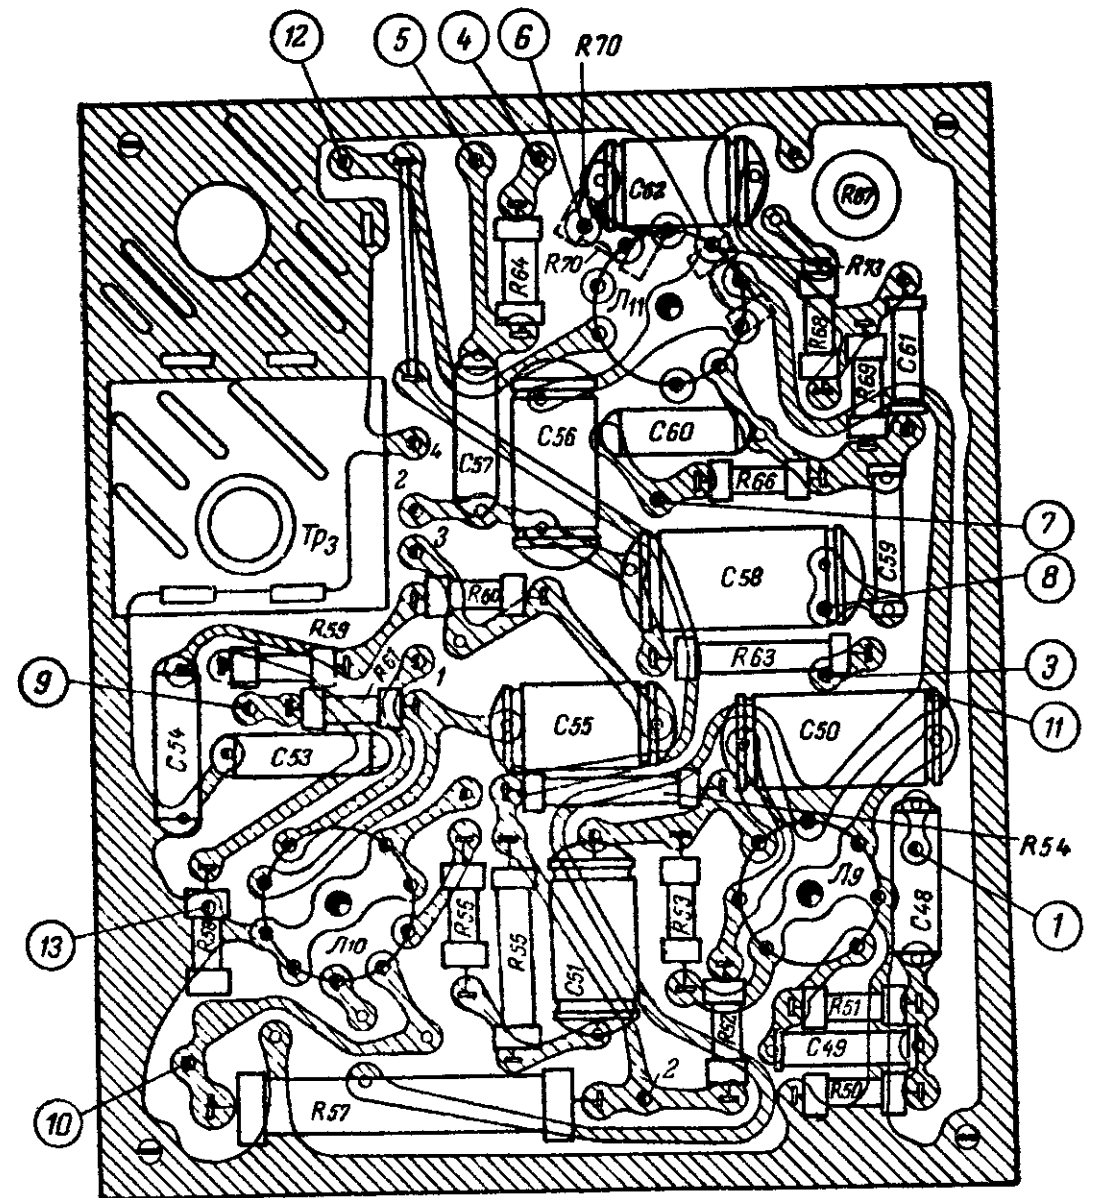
Расположение деталей и печатного монтажа на плате кадровой развертки телевизора «Старт-3».
